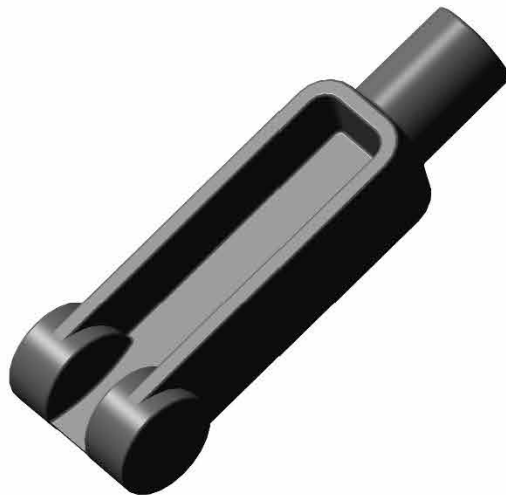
Параметрична тривимірна твердотільна модель поковки "Вилка"
